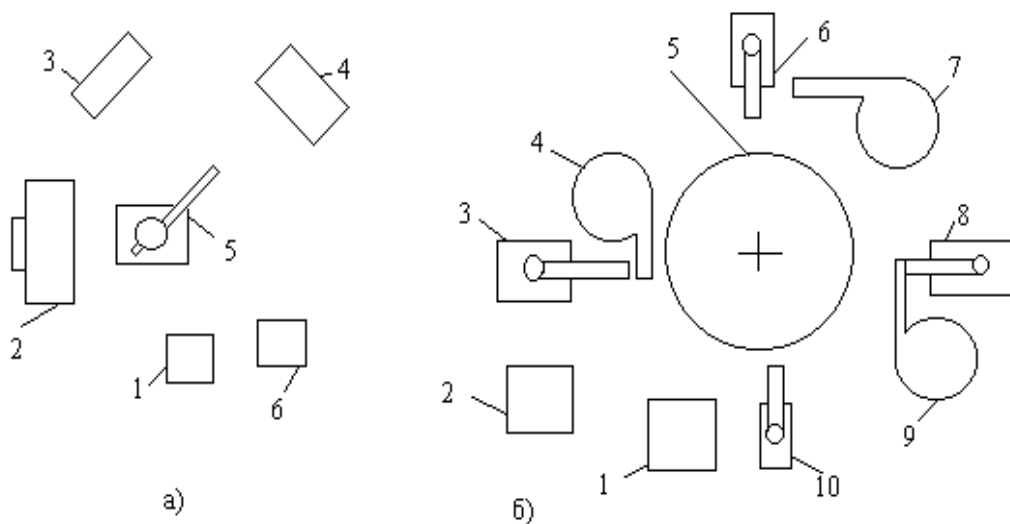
РТК сборки круговой компоновки: а - с расположением ПР в центре:
